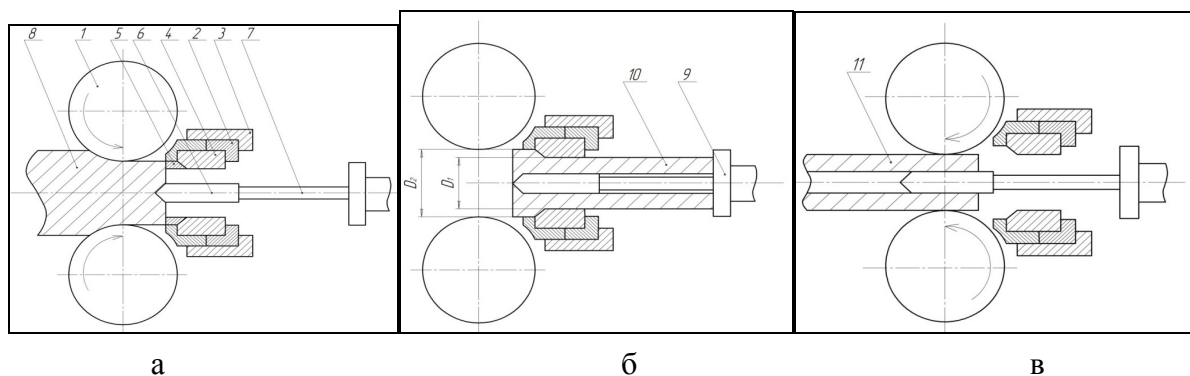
Схема процесса «прокатка – прошивка – прессование»
